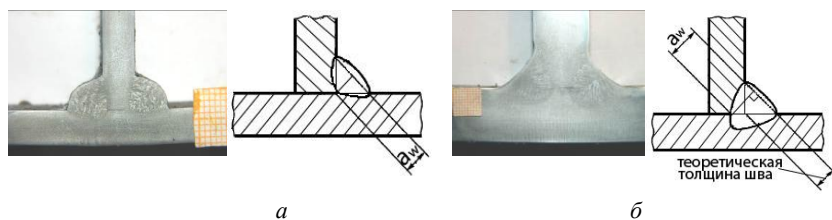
Сварные соединения с конструктивно неполным проплавлением
